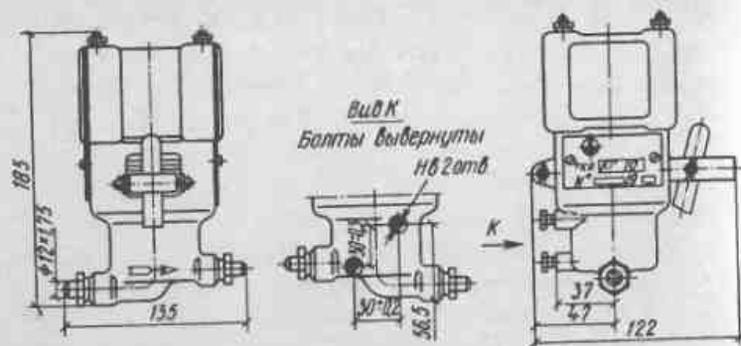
Общий вид и габаритные размеры электромагнитного клапана КГ-10
